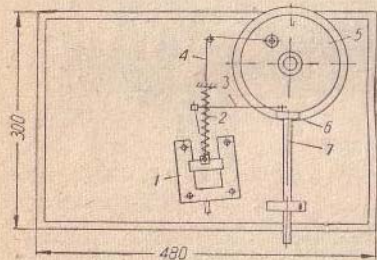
Кинематическая схема приспособления для механического перемещения щупа.
